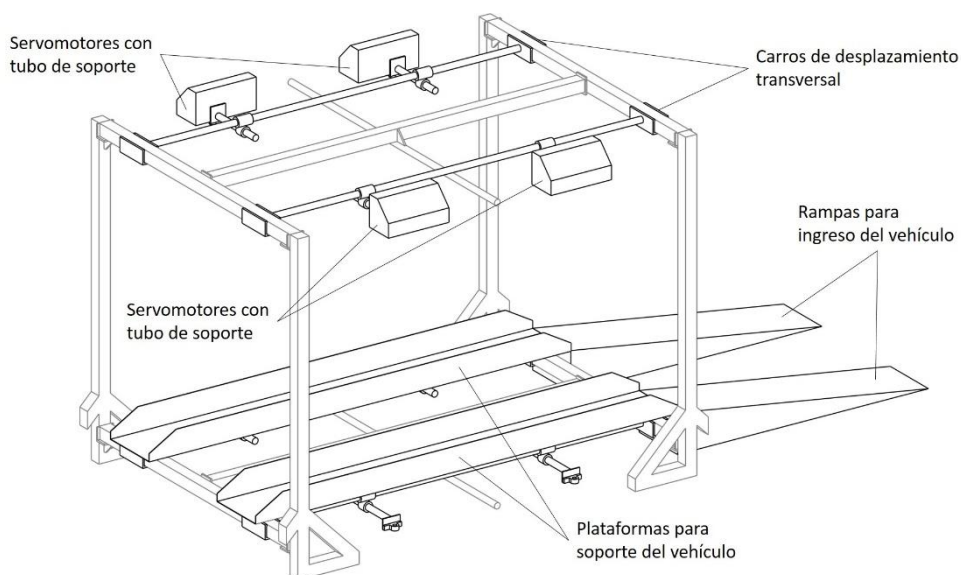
Vigas transversales de la estructura del Banco KLT.
